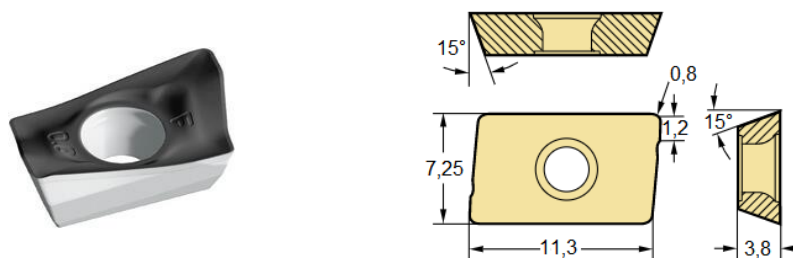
Geometria e dimensões (em milímetros) do inserto Tiger-tec® Silver ADMT [Walter Tools, 2021].
